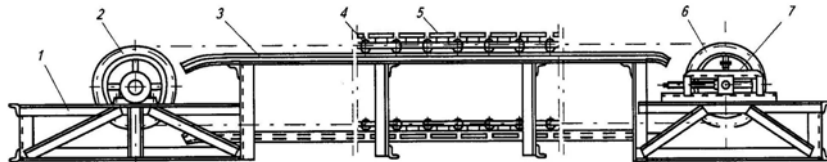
Схема пластинчастого конвеєра: 1 – металева рама; 2 – приводні зірочки; 3 – напрямні; 4 – тяговий елемент ланцюга; 5 – пластини; 6 – натяжні зірочки; 7 – гвинтова натяжна станція
